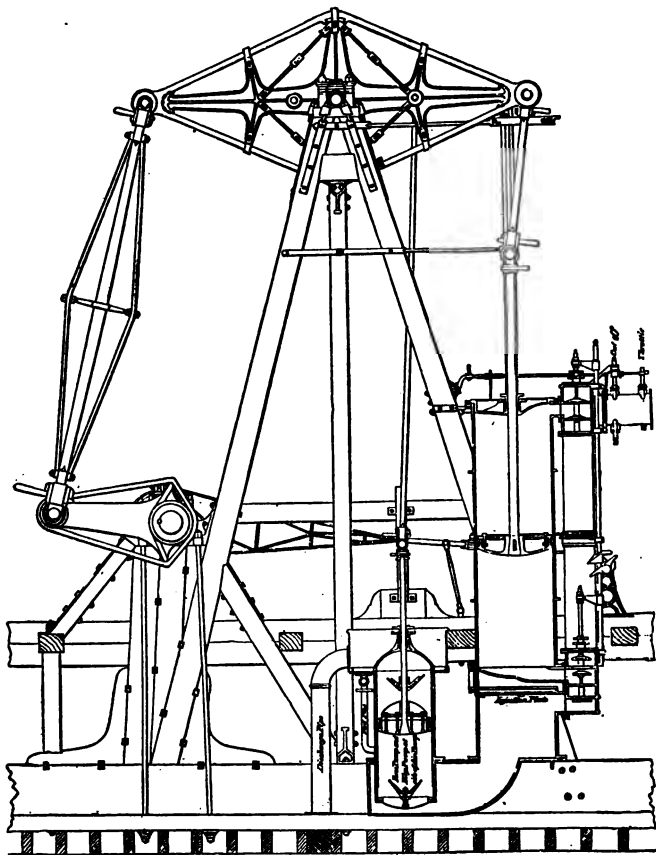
Machine à balancier supérieur d'un bateau de rivière américain; cylindre unique, distribution par soupapes. Ces machines, d'un type ancien, se trouvent encore aujourd'hui en service sans modifications essentielles.
